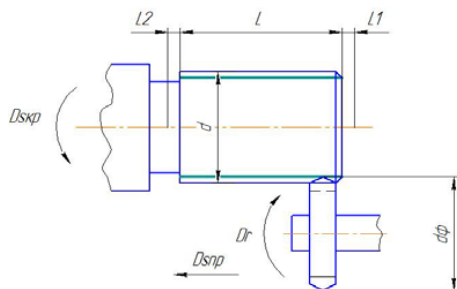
Фрезерование резьбы дисковой фрезой
